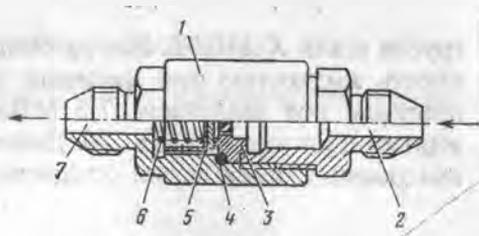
Обратный клапан 988А4: 1 - корпус; 2, 7 - штуцера; 3 - седло; 4 - уплотнительное кольцо; 5 - колпачок с резиновой шайбой; 6 - пружина
